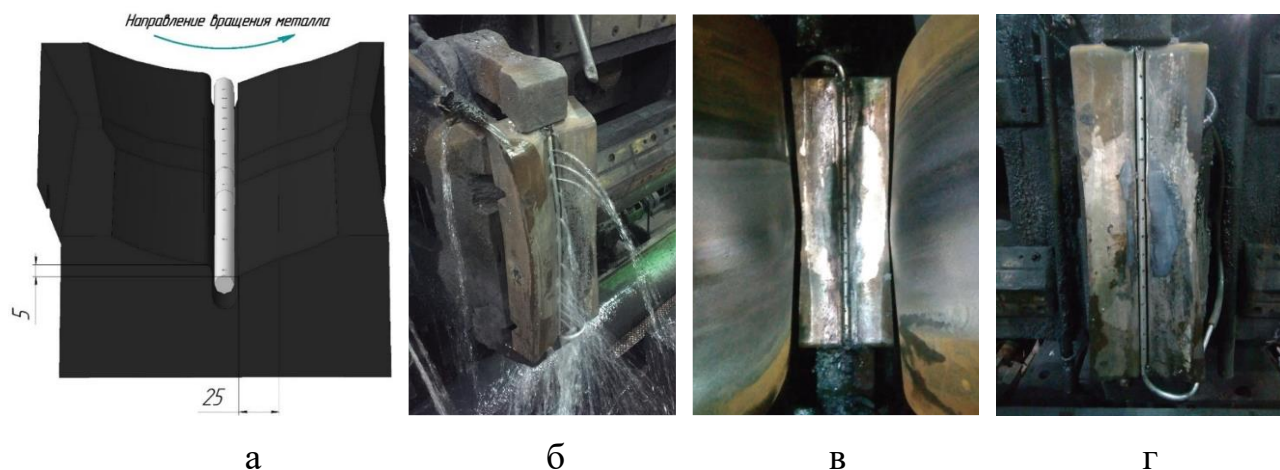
Конструкция направляющих линеек с подачей охладителя непосредственно на рабочую поверхность инструмента в процессе прокатки:
